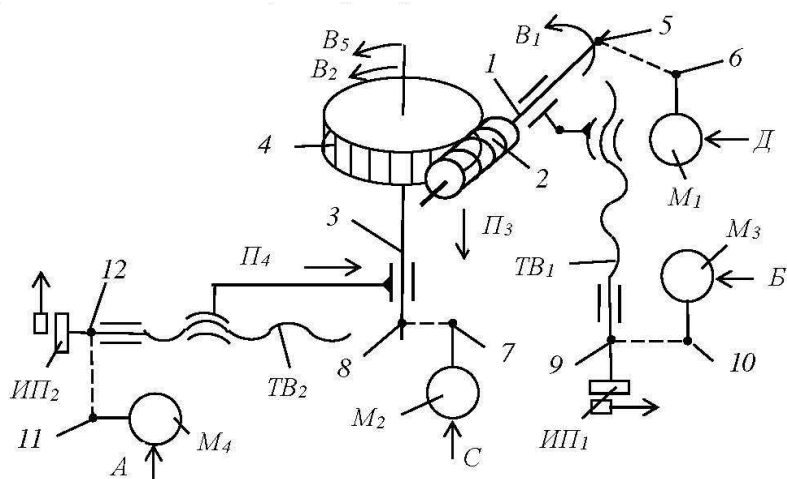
Схема приводов зубофрезерного станка для обработки колес с наклонными зубьями
